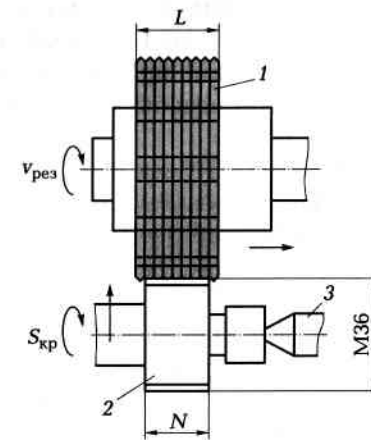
Схема нарезания резьбы дисковой фрезой
